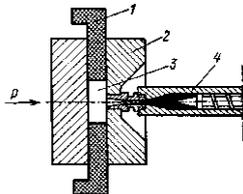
Схема сварки расплавом полимера:
